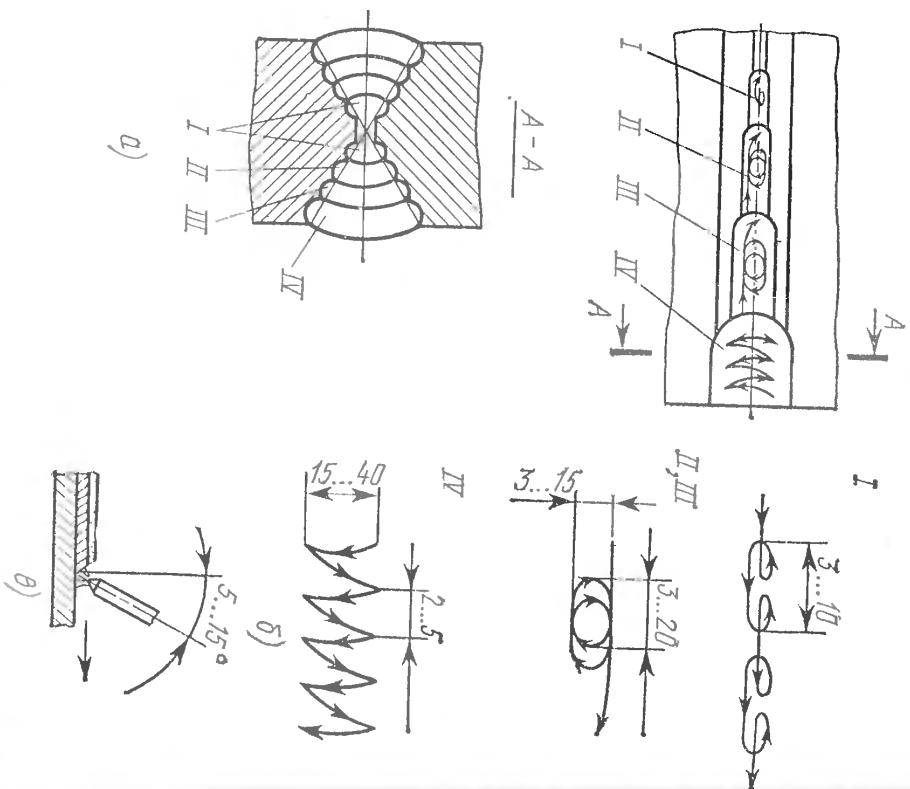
Траектория движения и размеры колебаний горелки при наложении многослойных стыковых швов в процессе сварки в углекислом газе:
